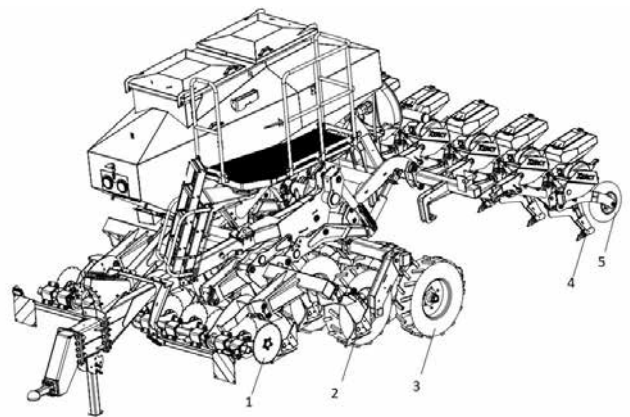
Схема робочої секції двопрохідного Strip-till агрегату яка складається: 1-дисковий очисник ряду; 2-прорізаючи диск; 3-розпушувальна стійка; закриваючі диски
